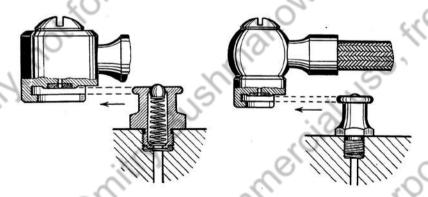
Schmiernippel mit aufzusetzendem Mundstück links große Ausführung (im Schnitt) rechts kleine Ausführung
